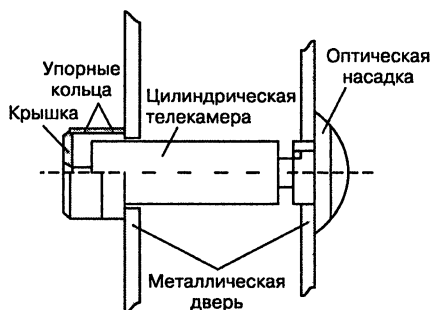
Крепление видеоглазка в металлическую пустотелую дверь с помощью крышки с упорными кольцами
